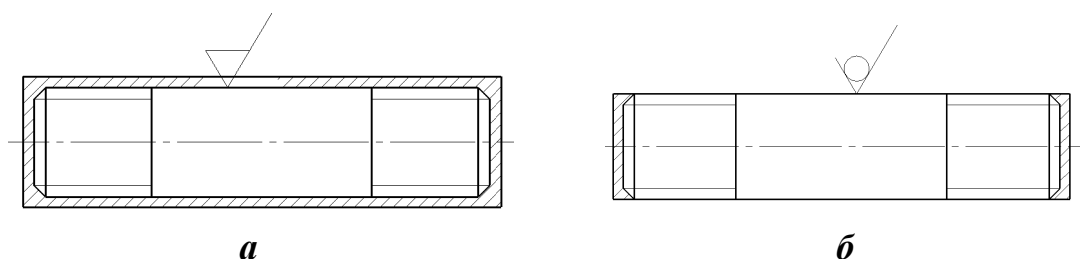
Шпилька, виготовлена обробкою різанням (а) та накатуванням (б)
